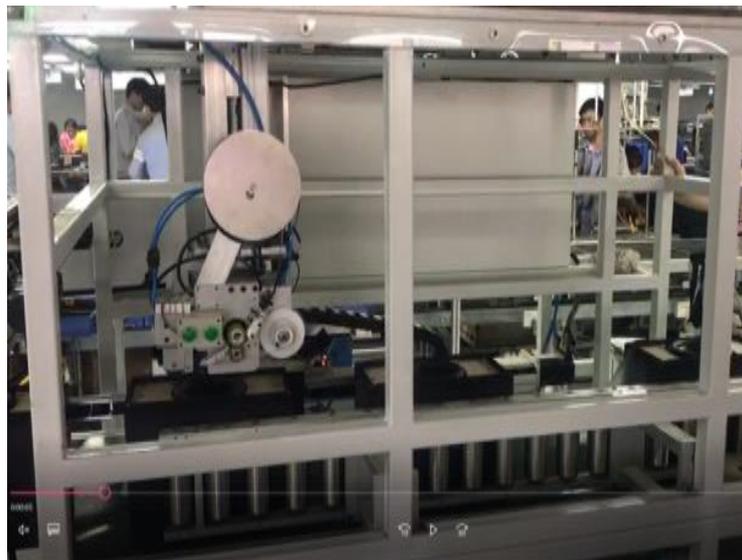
Proposta de Aplicação Automática da Aplicação de Vedação.
